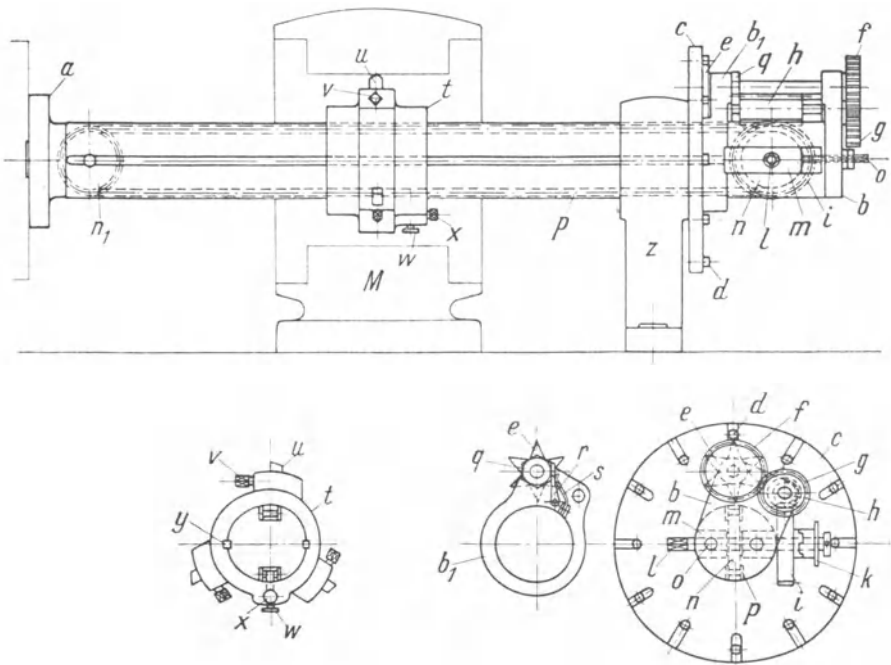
Ausbohrvorrichtung für Motorgehäuse auf schweren Bohrwerken.
